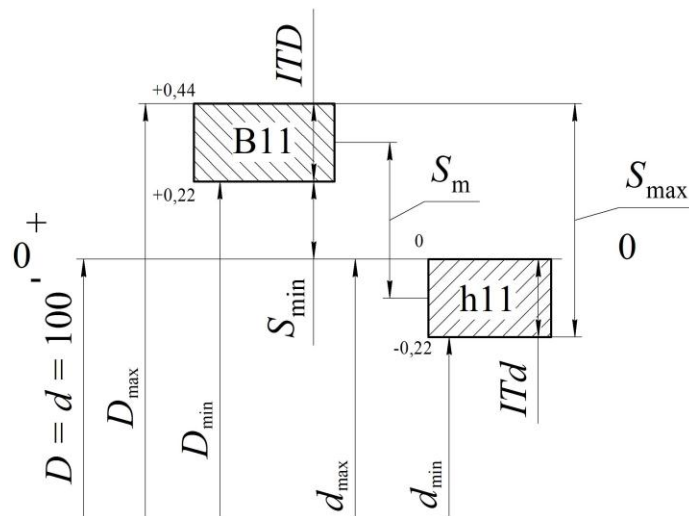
Схема расположения полей допусков посадки с зазором
